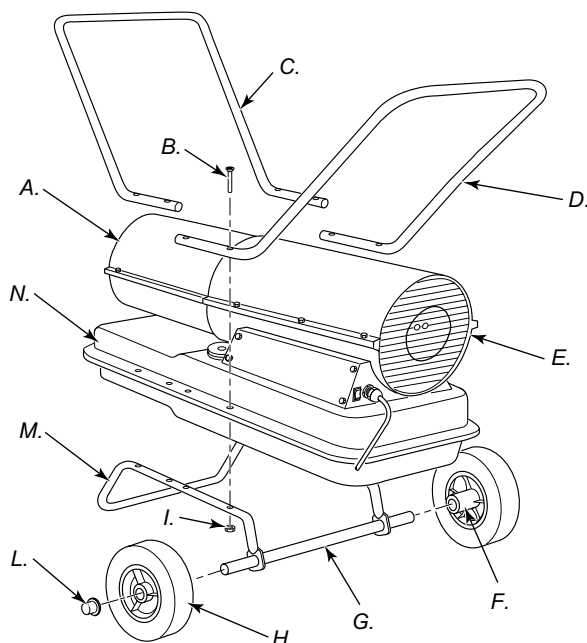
Assemblaggio ruote ed impugnature per i modelli 30 kW e 43 kW.
